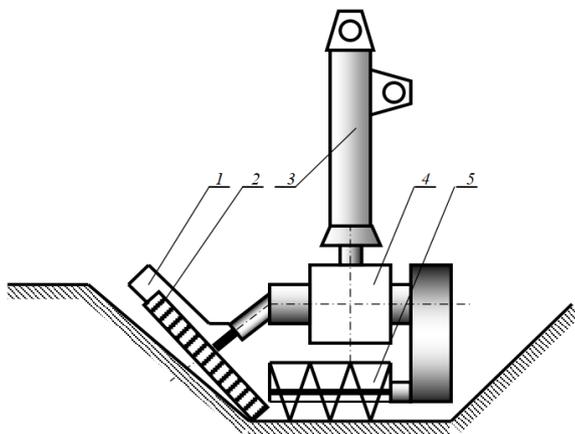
Схема комбинированного шнекофрезерного рабочего органа с цилиндрическим шнеком: 1 — кожух; 2 — дисковая фреза; 3 — рукоятка; 4 — редуктор гидропривода; 5 — цилиндрический шнек
